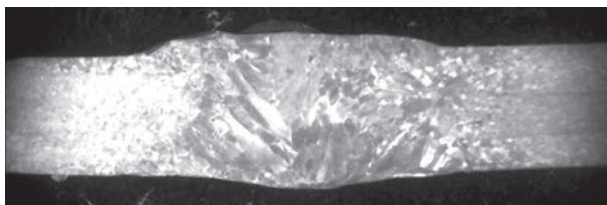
Поперечний макрошліф зварного з'єднання псевдо-β титанового сплаву VT19, виконаний TIG зварюванням із застосуванням присадного дроту
